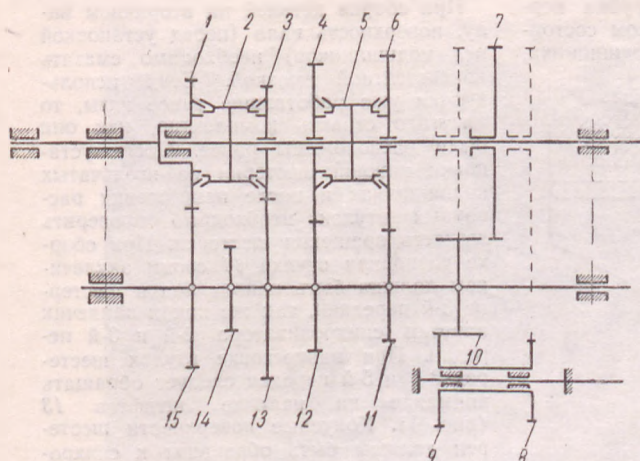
Кинематическая схема трехходовой пятискоростной коробки перемены передач автомобиля ЯАЗ-200:
